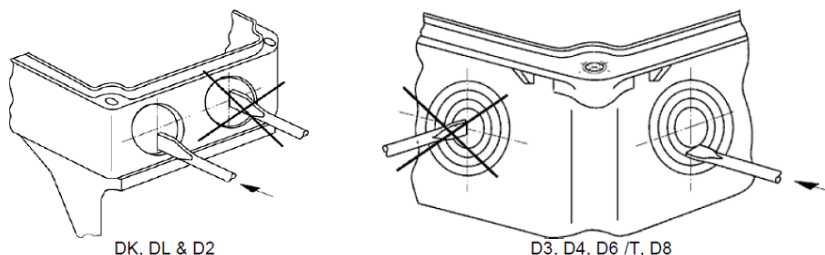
Bearbeitung des Anschlusskastens zum Einbau der Verschraubung - Achten Sie auf die Positionierung des Schraubendrehers
